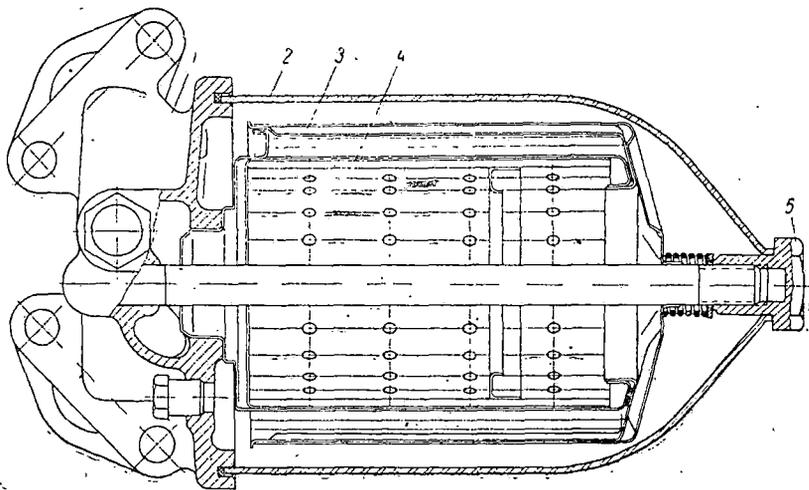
Фильтр грубой очистки масла двигателей ЯМЗ:
